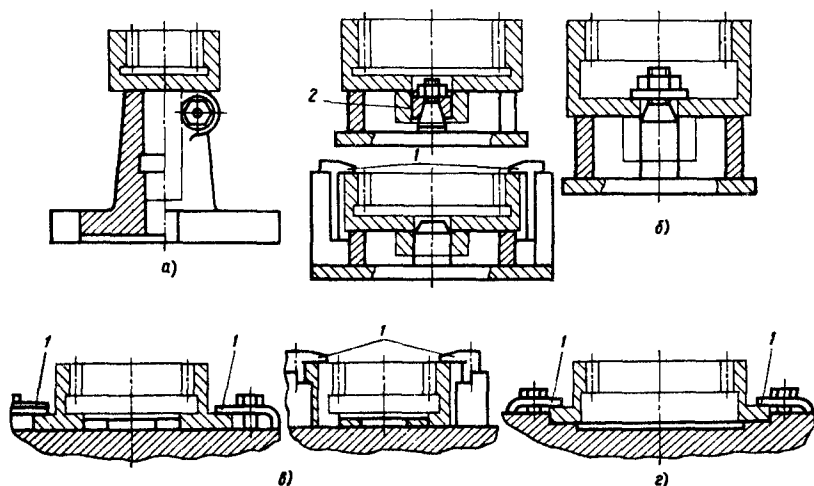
Схемы установки заготовок колес с внутренними зубьями на зубообрабатывающих станках:
